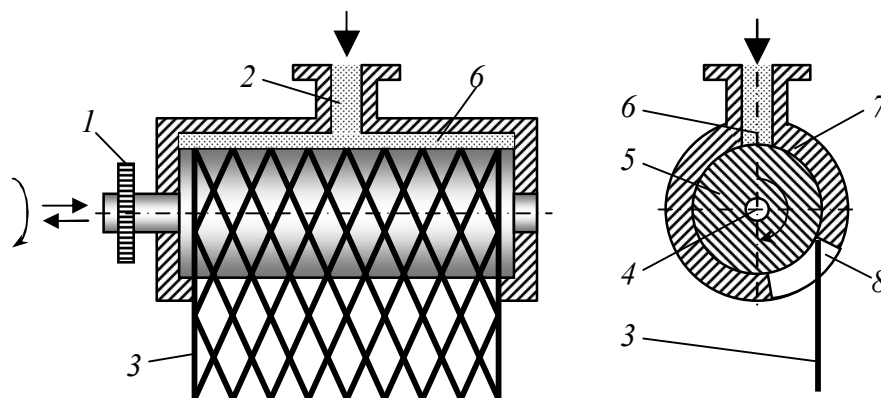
Способ получения полимерных сеток заполнением расплавом рельефного узора на поверхности вращающегося цилиндра: 1 – шестерня цилиндра; 2 – подводящий канал; 3 – готовая сетка; 4 – осевой канал цилиндра; 5 – формующий цилиндр; 6 – камера; 7 – корпус с цилиндрической полостью; 8 – выпускное окно корпуса
